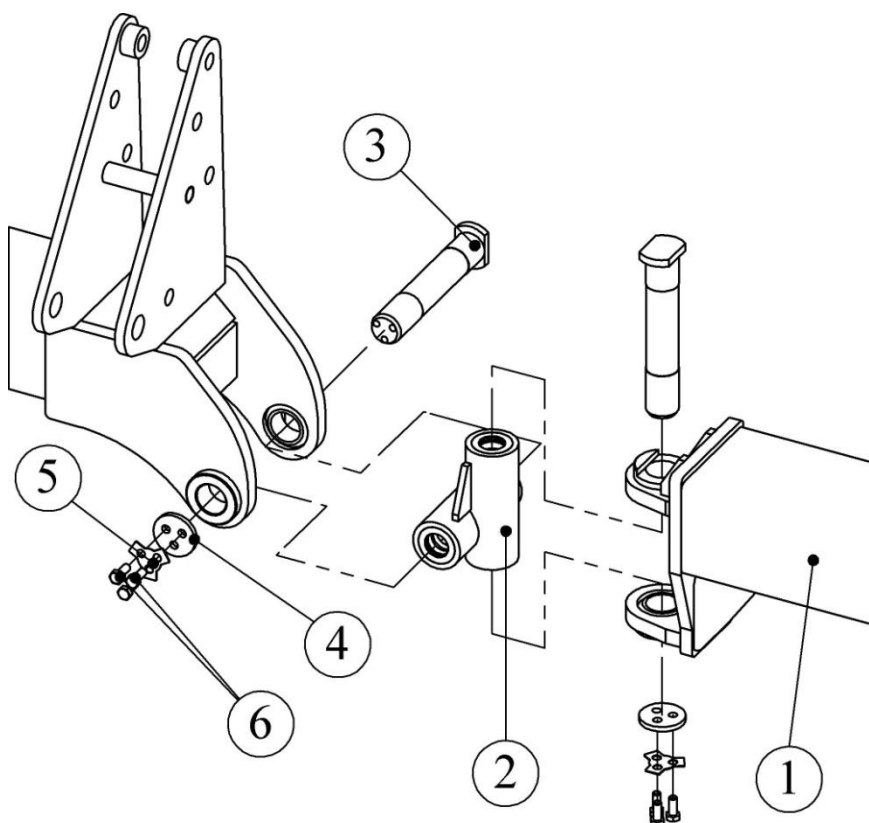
Детали крепления боковой балки после 06.2019.
